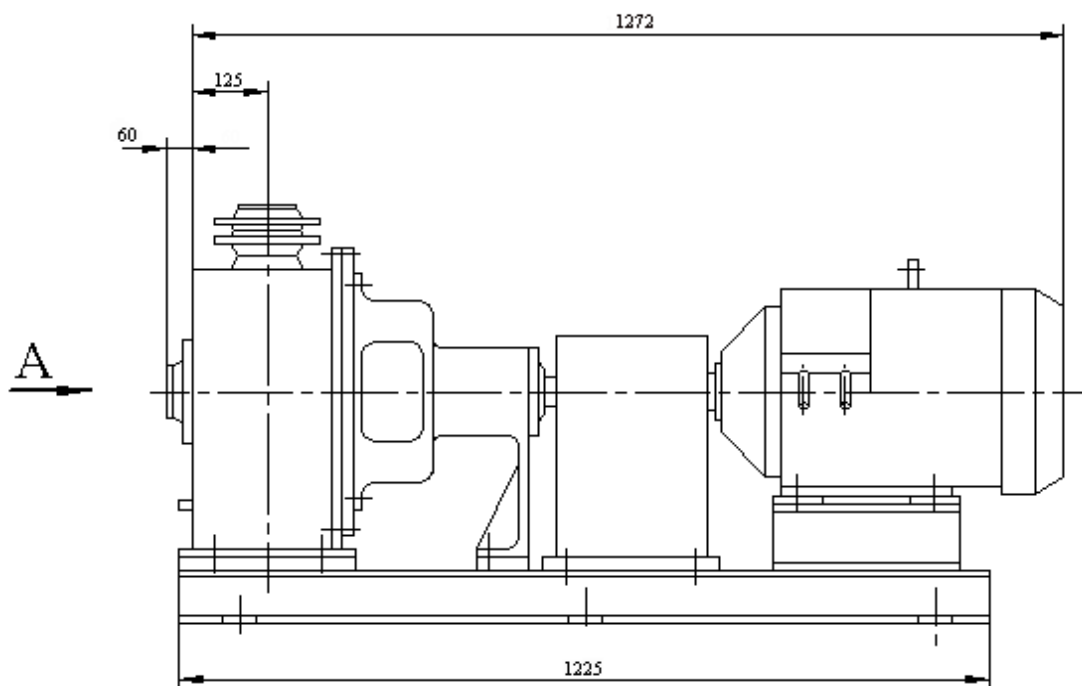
Габаритный чертеж насосного агрегата типа ЦНА 6,3/50
